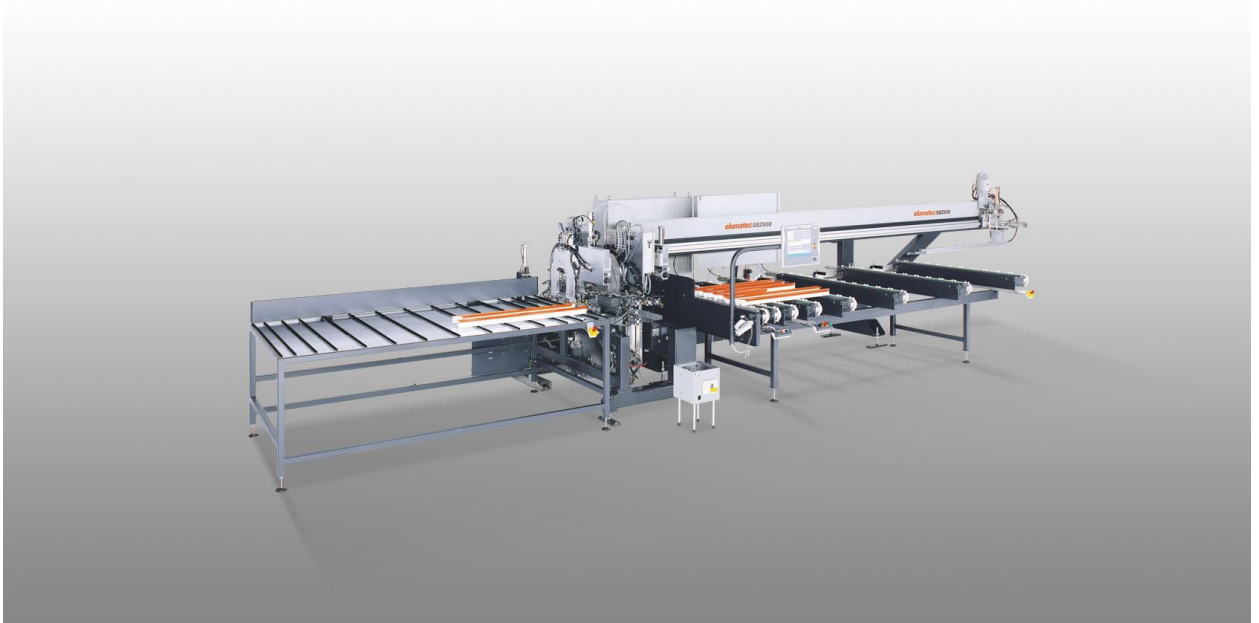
Обрабатывающий центр Elumatec SBZ-608⁵
